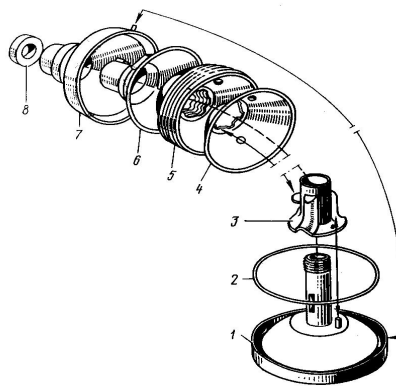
Детали барабана сепаратора (по ходу сборки):
